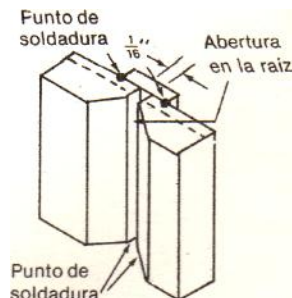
Unión del conjunto a ser soldado con prensa o puntos de soldadura.
